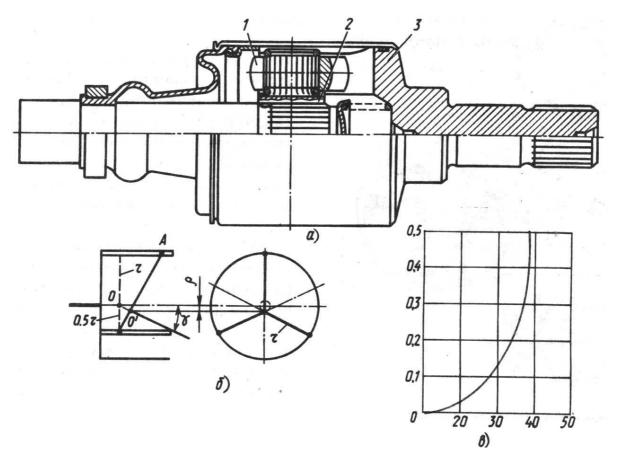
Трехшиповой универсальный карданный шарнир: a – конструкция;  $\delta$  – схема;  $\epsilon$  - характеристика
